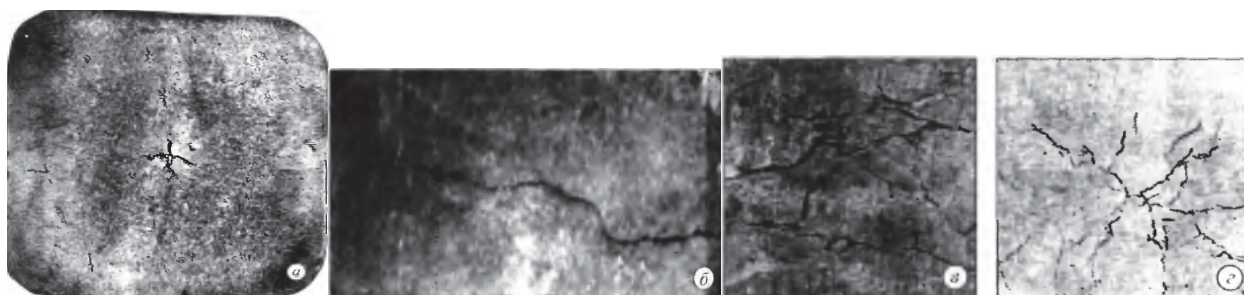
Горячие трещины в отливках (сталь):
